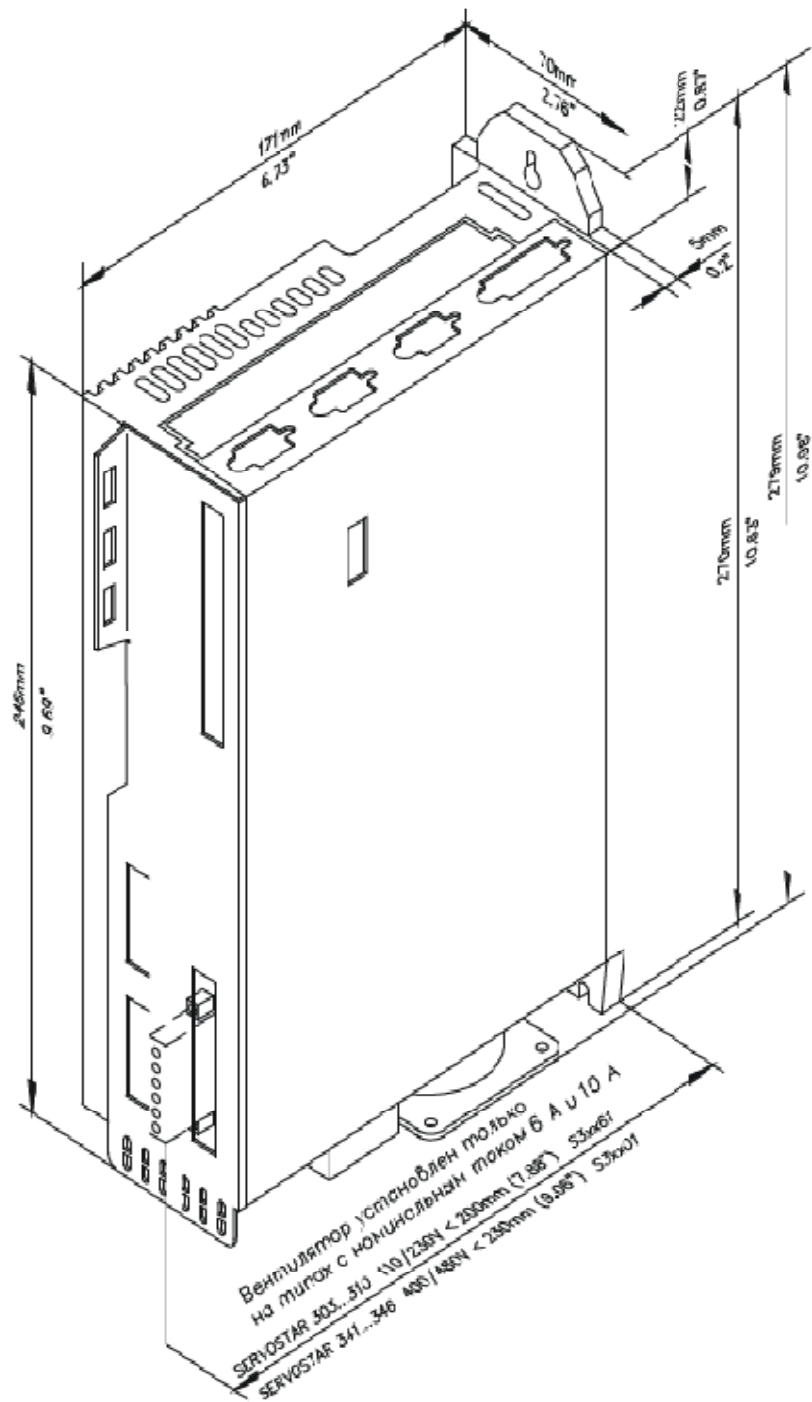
Габаритные размеры сервоусилителя S30361-NA
